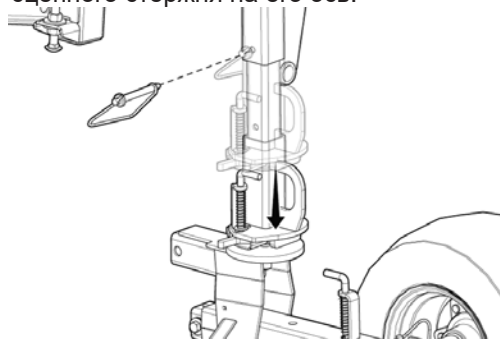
Опускание скобы сцепного стержня на ось сцепного стержня
